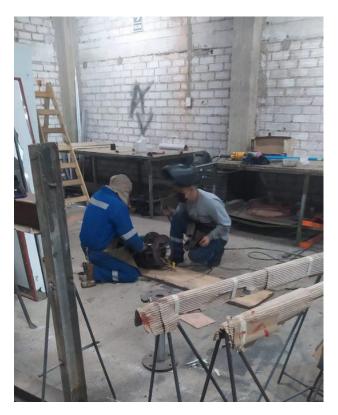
Operarios realizando una pieza del horno en soldadura. La empresa de investigación. Elaboración propia
